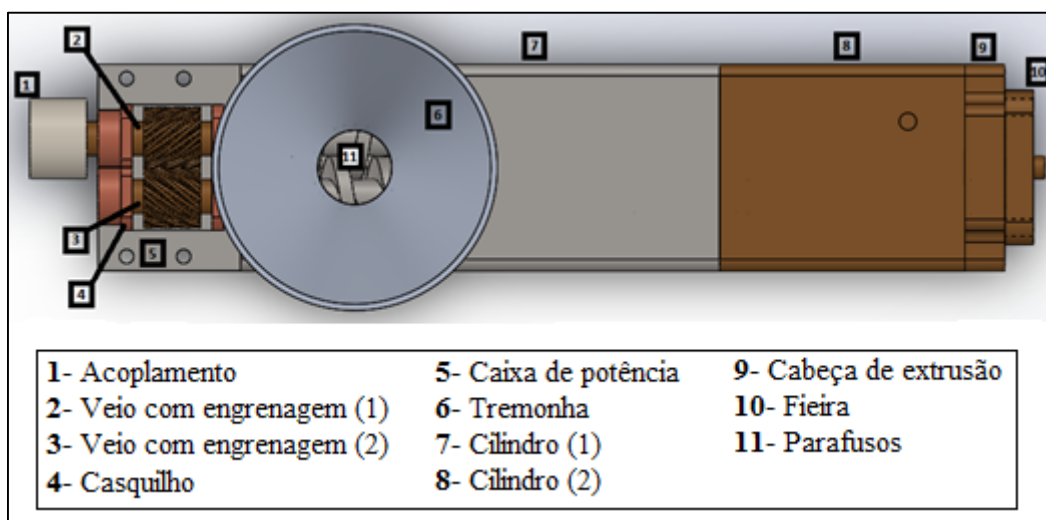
Componentes constituintes da mini-extrusora que seguiram para maquinagem
